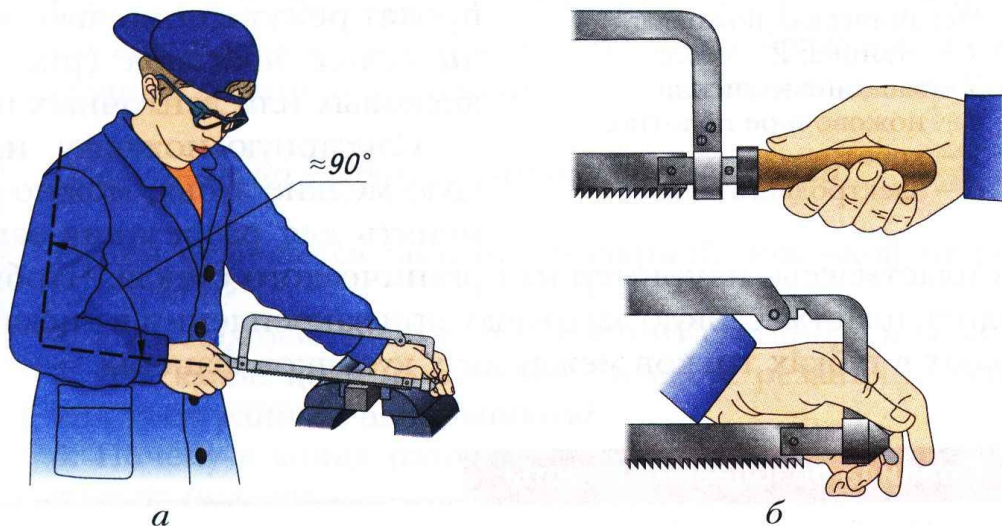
Работа ножовкой: *а* — положение корпуса; *б* — положение рук
